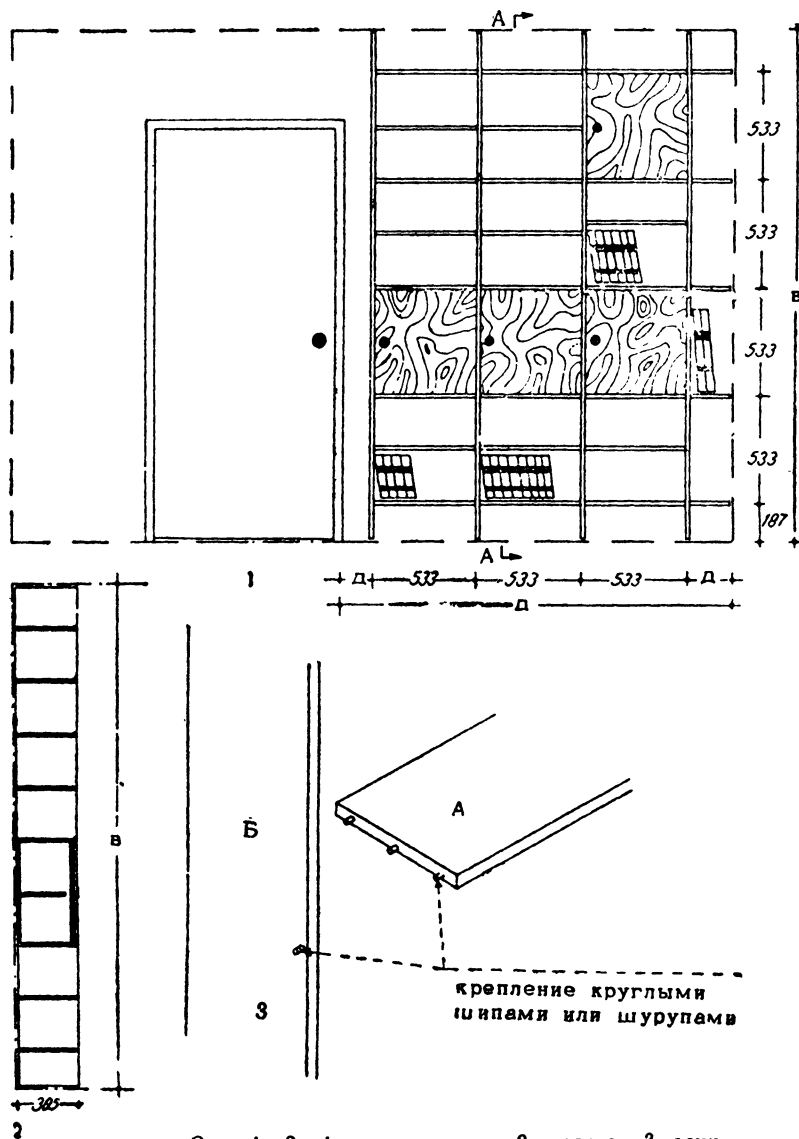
3. 1—вид спереди; 2—разрез; 3—эскиз соединения боковой стенки с полкой.
